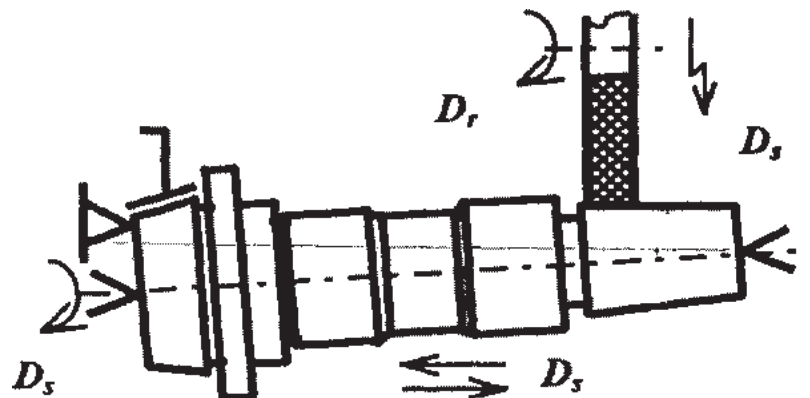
Схема обработки длинной конической поверхности с поворотом стола шлифовального станка
